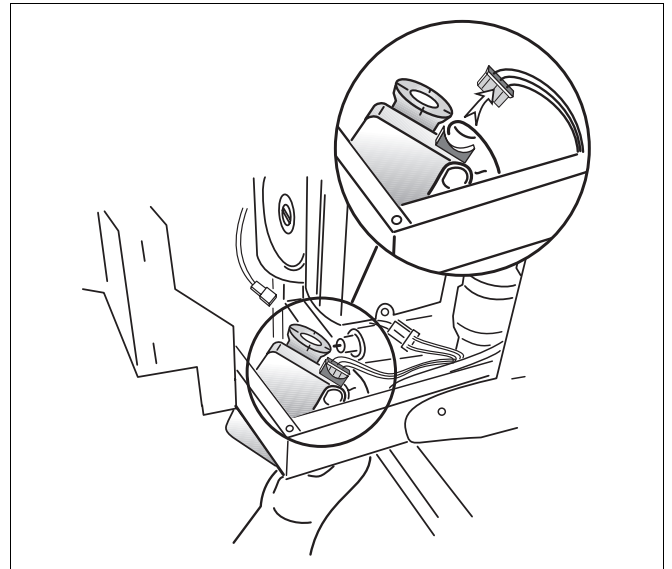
Steckkontakt vom Motor des internen Dreiwegeventils abziehen
